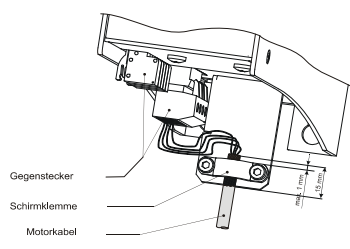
Sicht auf Motorgegenstecker der Serie SM (Gewinde M40)
